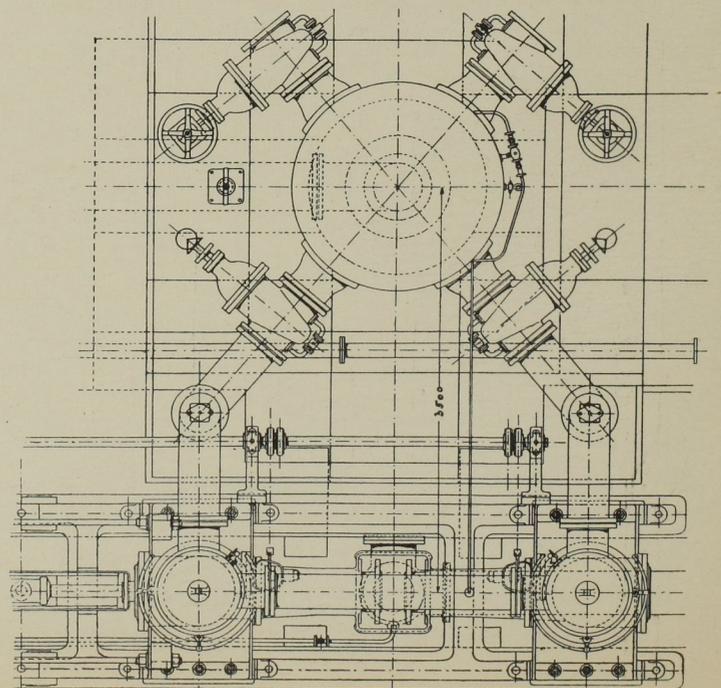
Grundriss und Rohrplan. Massst. 1:60.
